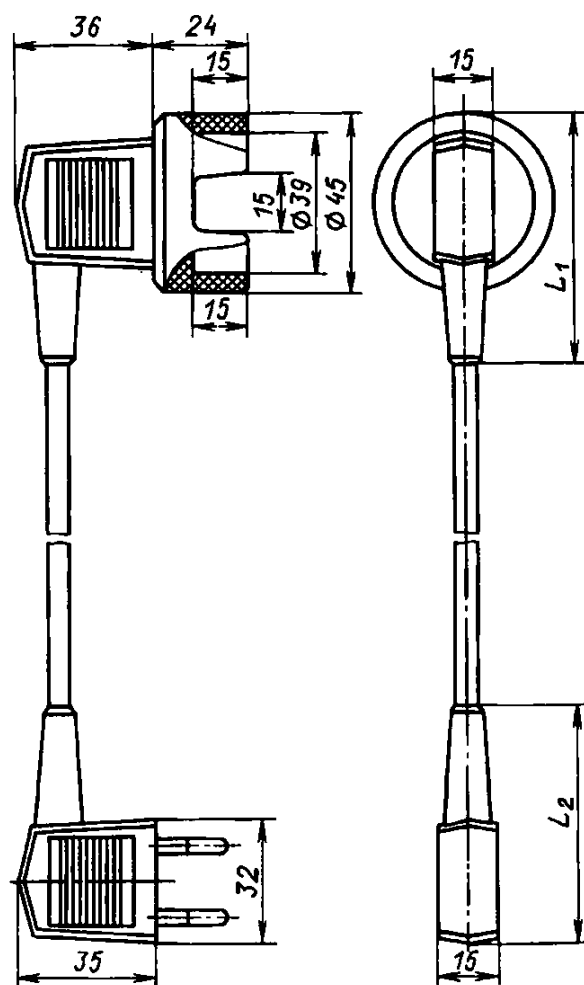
Концевая заделка удлинителя, армированного штепсельными вилкой и розеткой для бокового соединения
